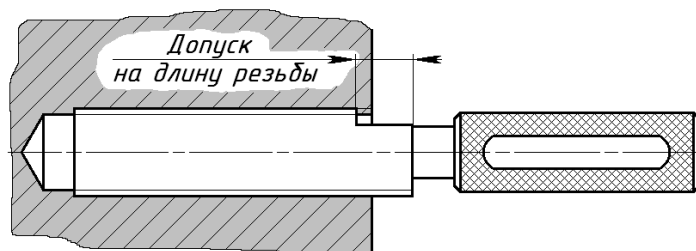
Схема контроля глубины резьбы в глухом отверстии
